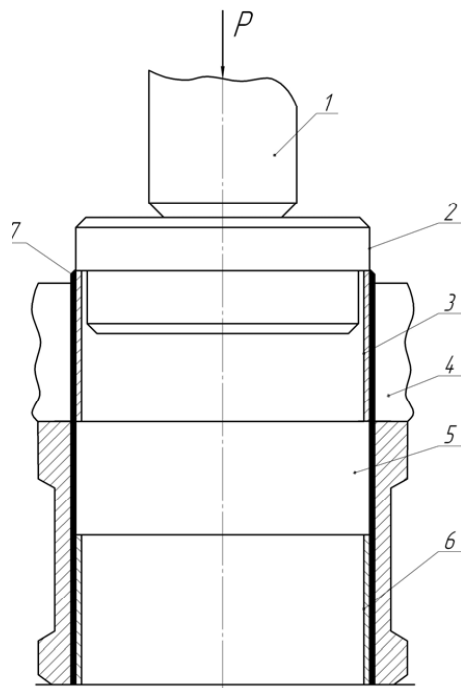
Схема запрессовки пластины в гильзу цилиндра: 1 – шток пресса; 2 – ступенчатый пуансон; 3 – свернутая пластина; 4 – матрица; 5 – восстанавливаемая деталь; 6 – первый пояс пластины
